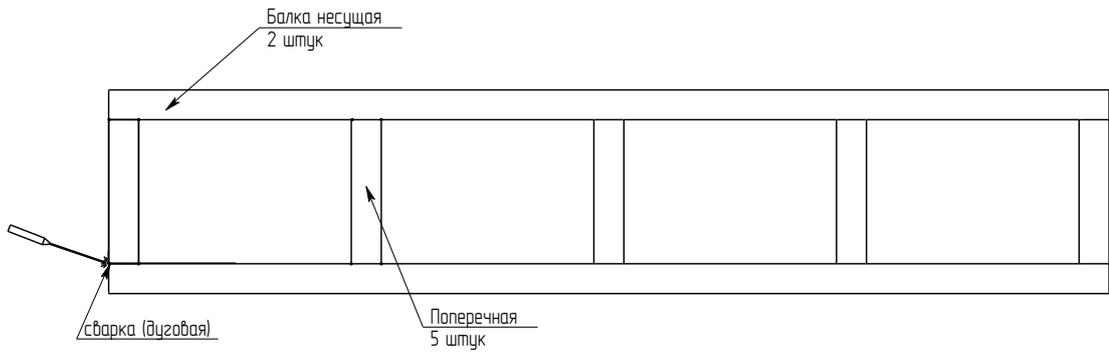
Соединение несущей балки и поперечной трубы с помощью сварки
